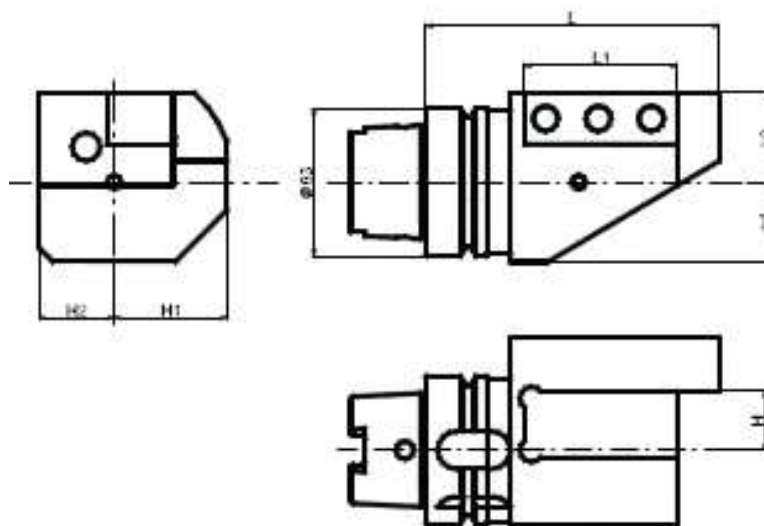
Резцедержатель HSK Holder HSK-A63W-ETV25x25R-125
